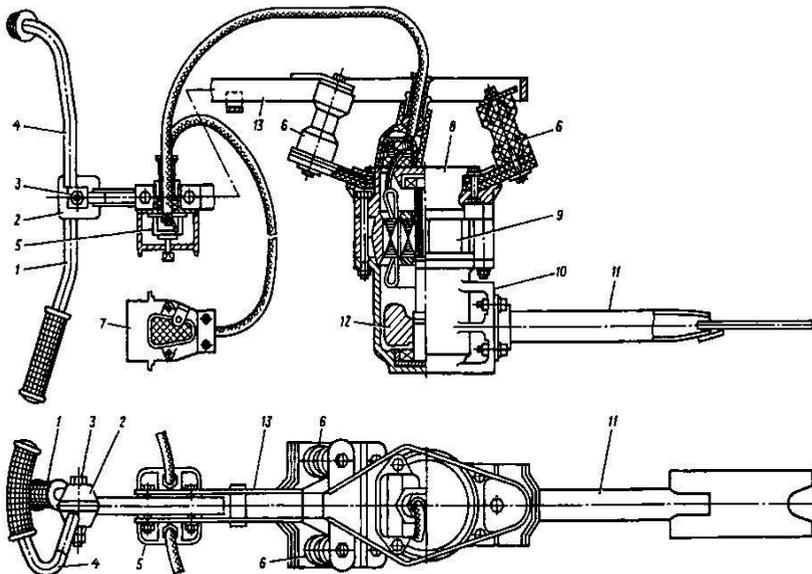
Электрошпалоподбойка ЭШП9МЗ: 1 – нижняя ручка; 2, 6 – амортизаторы; 3 – болт; 4 – верхняя ручка; 5 – выключатель; 7 – кабельная вилка; 8 – верхняя крышка; 9 – электродвигатель; 10 – корпус вибратора; 11 – подбивочное полотно; 12 – дебаланс; 13 – амортизационная рамка
